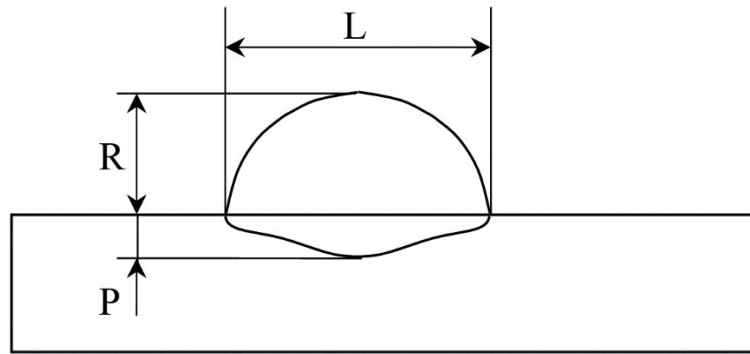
Medições realizadas no cordão de solda [Adaptada de 68].
